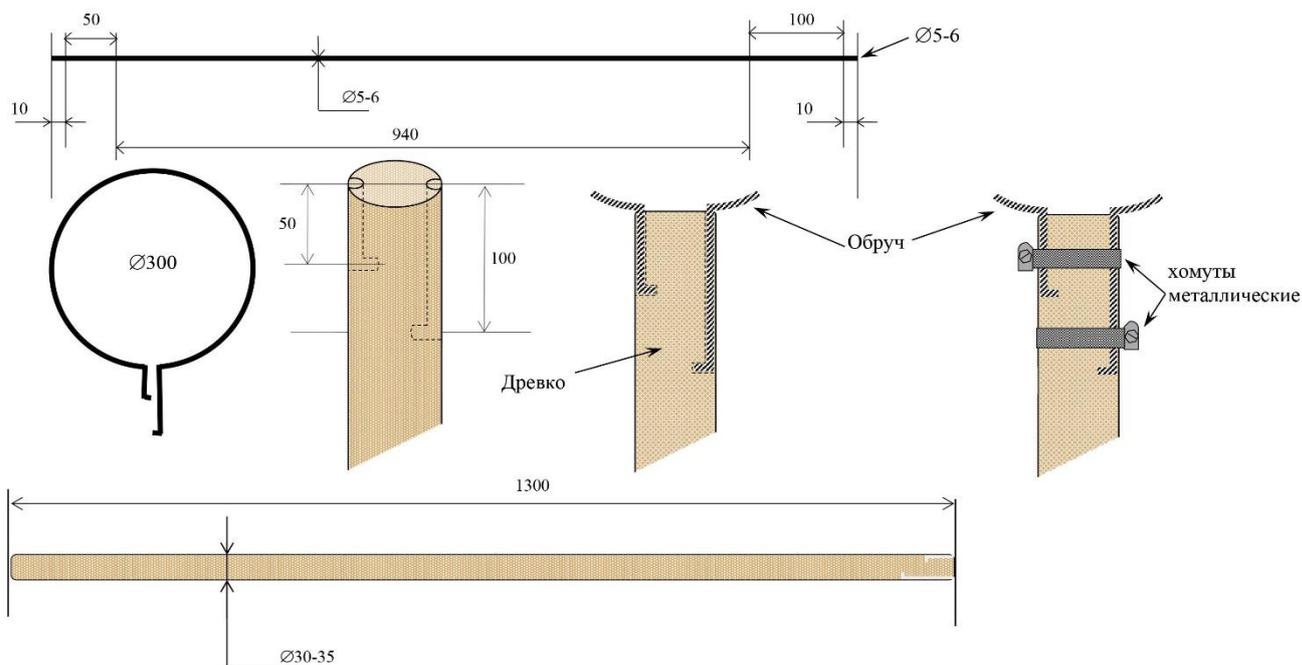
Изготовление обруча энтомологического сачка и его крепление.
